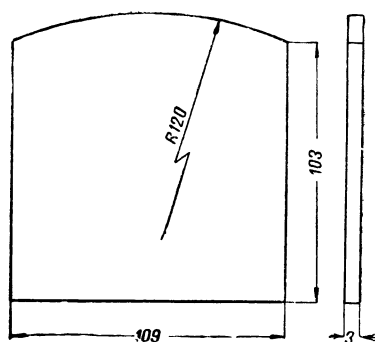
Вид кузова вагона с торца (лобовой стенки).
